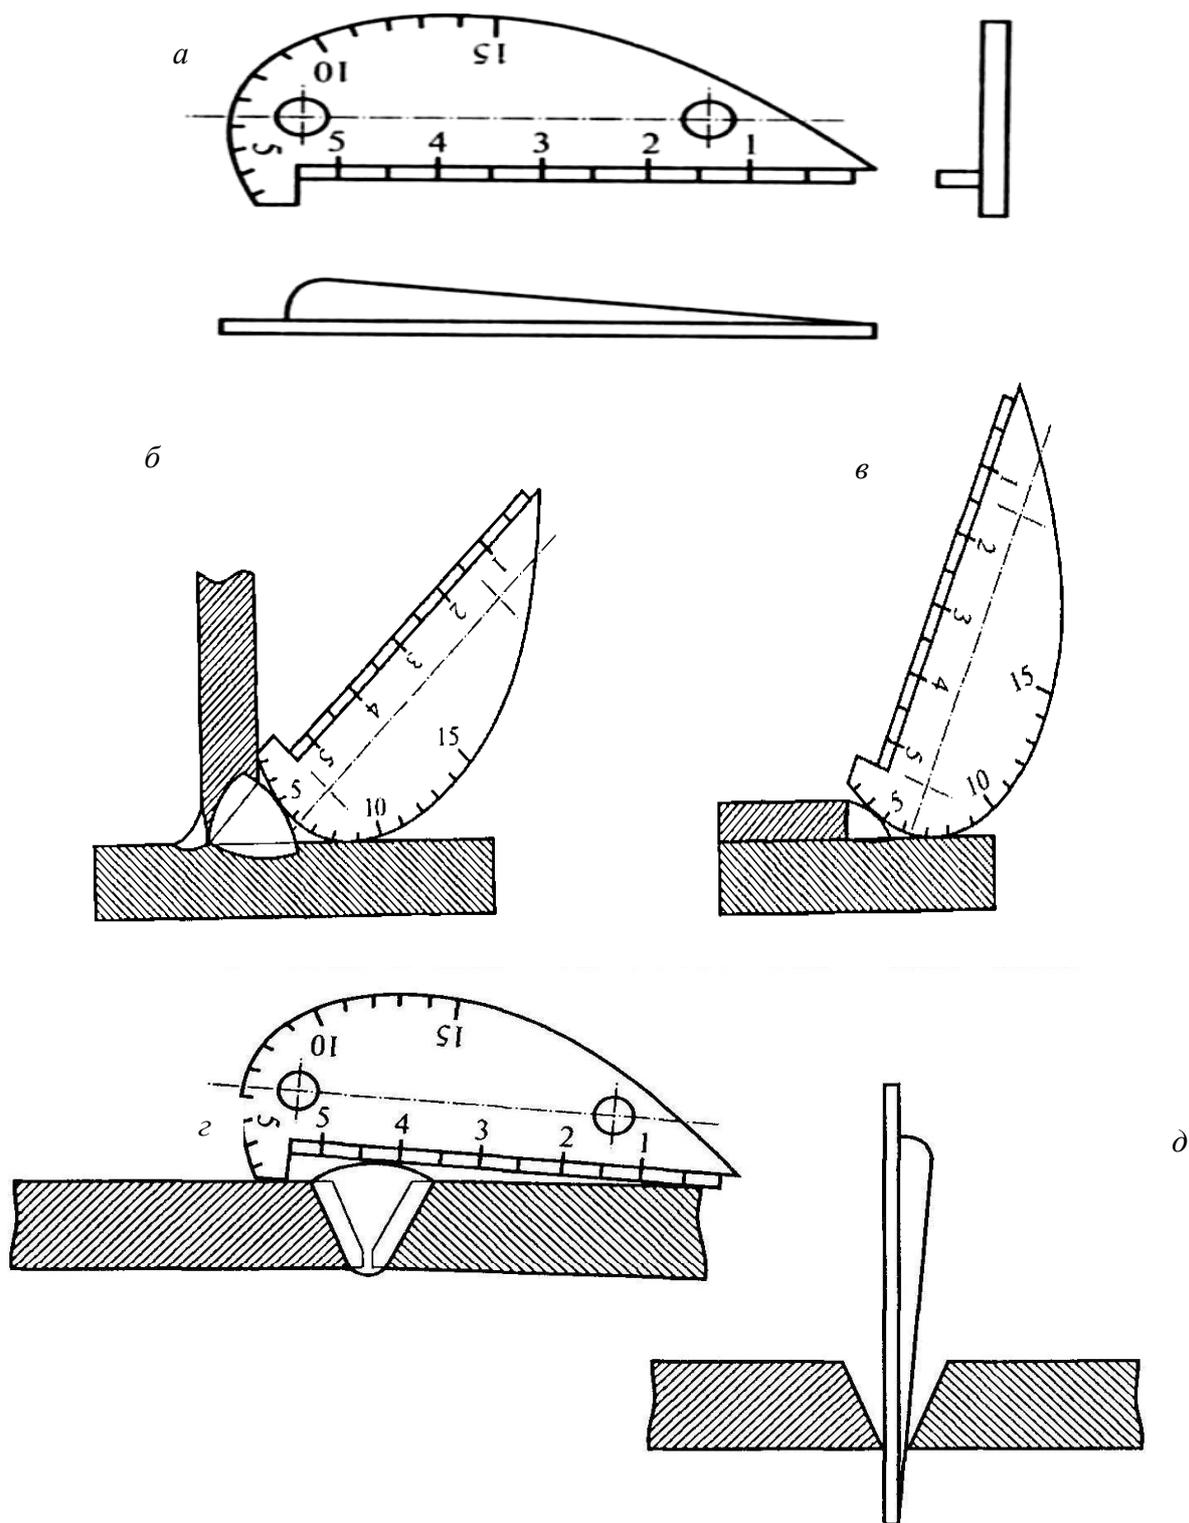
Контроль сварных швов шаблоном конструкции А.И. Красовского:
